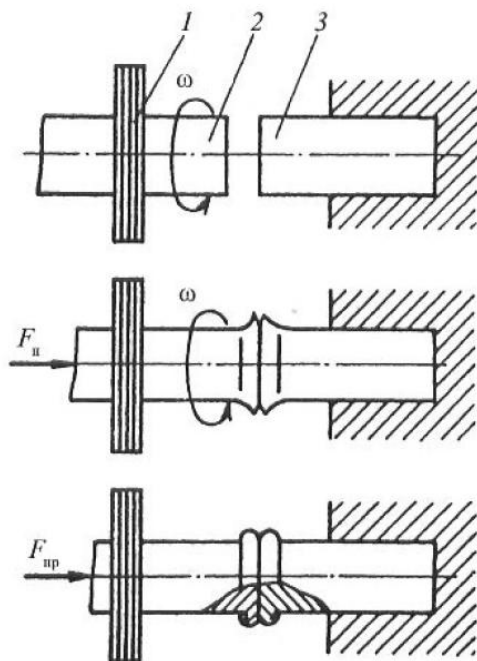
Схема сварки трением: 1 – маховик; 2,3 – свариваемые элементы
